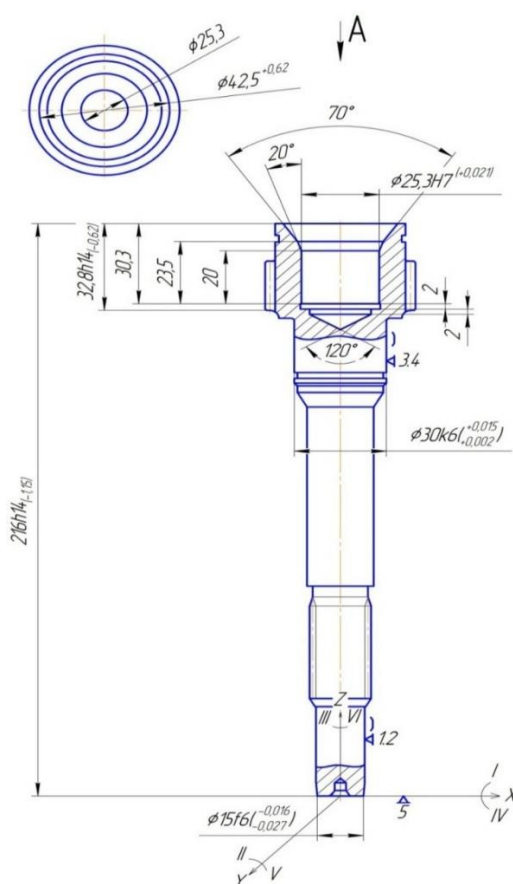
Схема базування заготовки в призмах (перший варіант)
